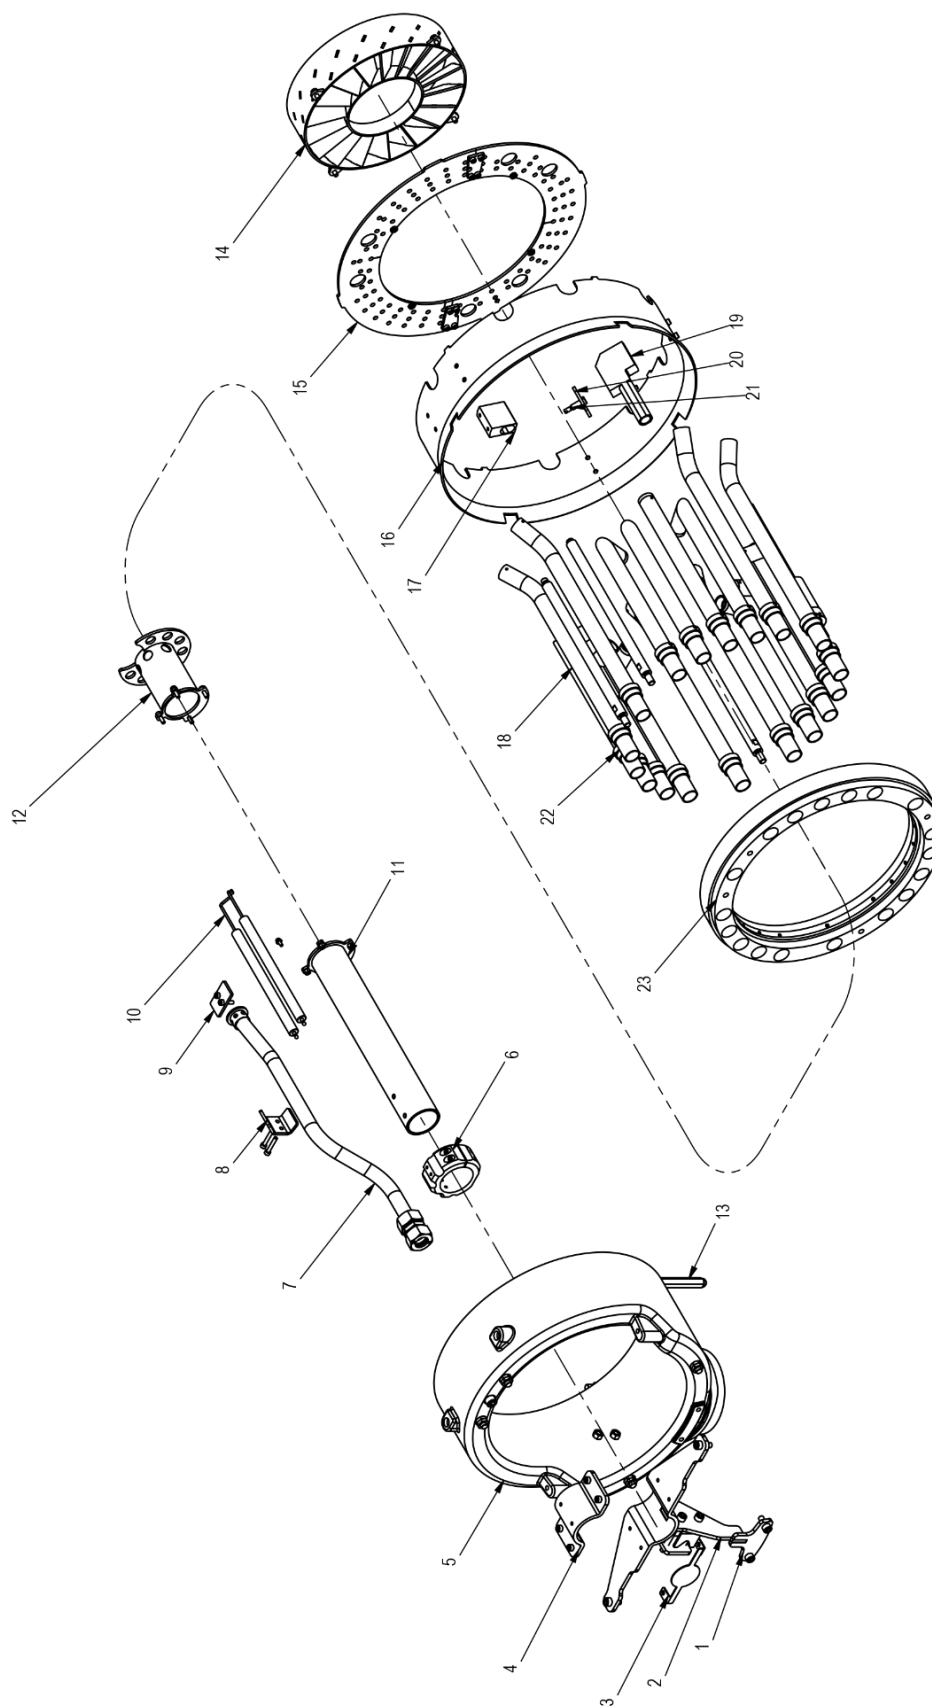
Вид элементов смесительного устройства горелки RGB-M-1350
